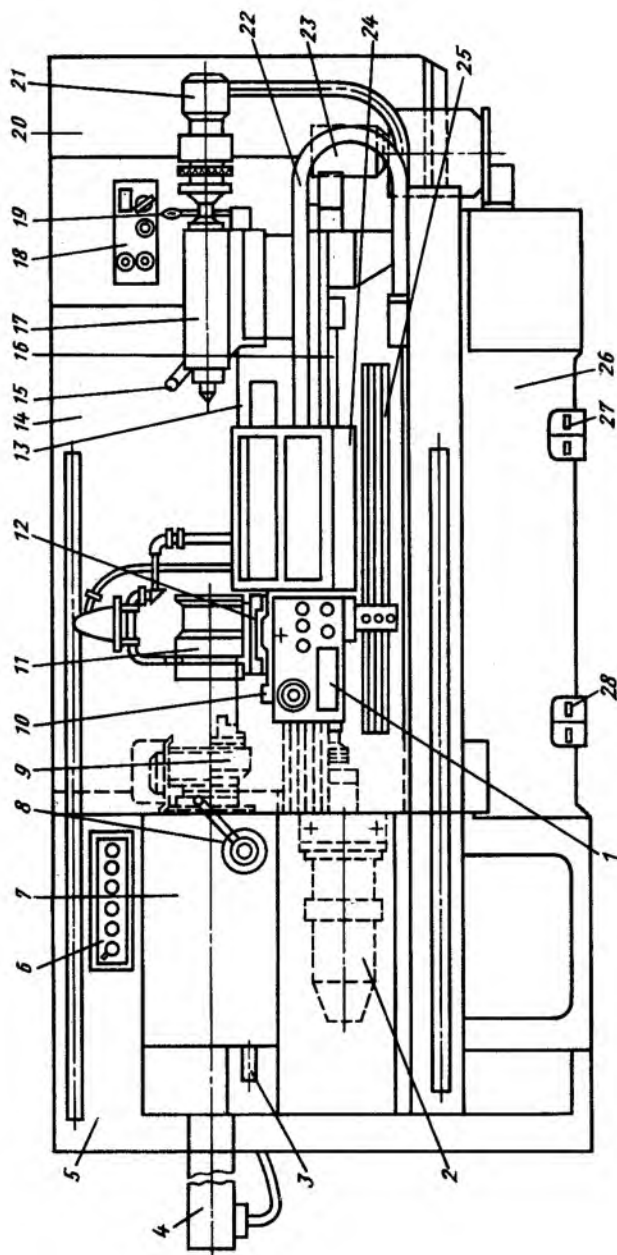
Токарный станок 16K20T1 с ЧПУ
